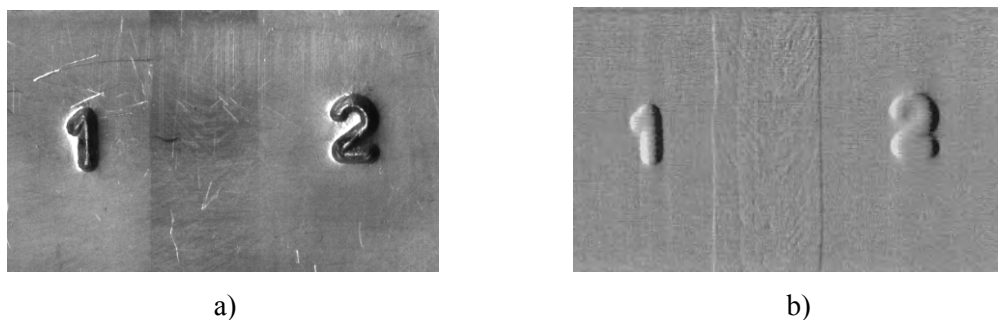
Изображение (а) и МО ВТ образ МГ (b) бездефектного сварного шва в алюминиевом сплаве.
